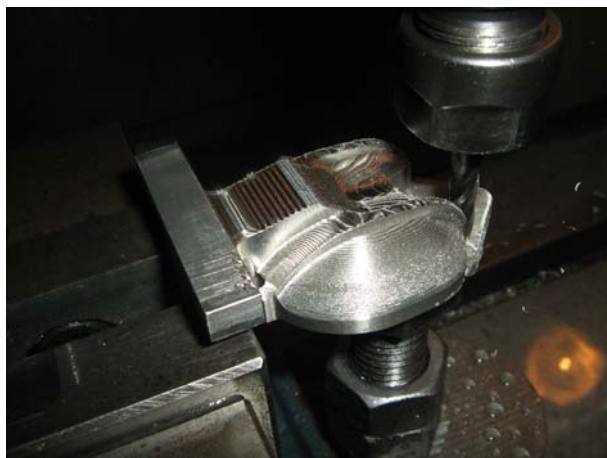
Maquinado álabe Pelton en Fresadora C.N.C
